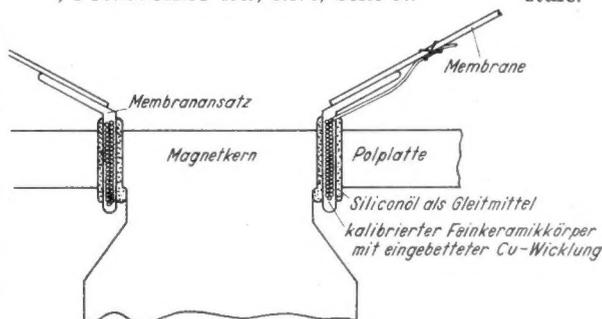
Schema einer dynamisch angetriebenen Lautsprecher-Schwingspule mit Siliconöl als Gleitmittel im extrem engen Magnetspalt
